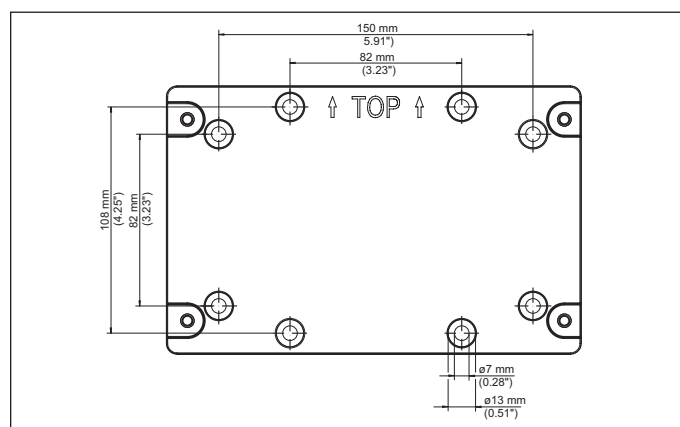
Монтажная панель для настенного монтажа (VEGAMET 861, 862)
